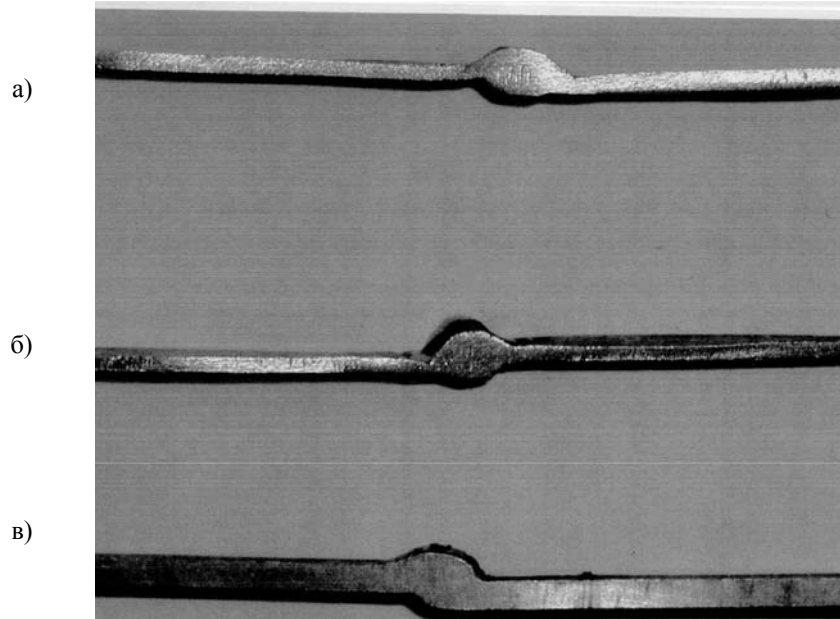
Сварные соединения, выполненные со смещением кромок: толщина образцов а и б – 1 мм; в – 2 мм; смещение кромок а – 0,58; б – 1,08; в – 0,88
